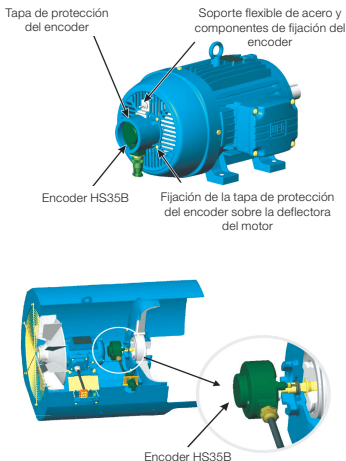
Montaje del encoder HS35B para motor autoventilado o con ventilación forzada
